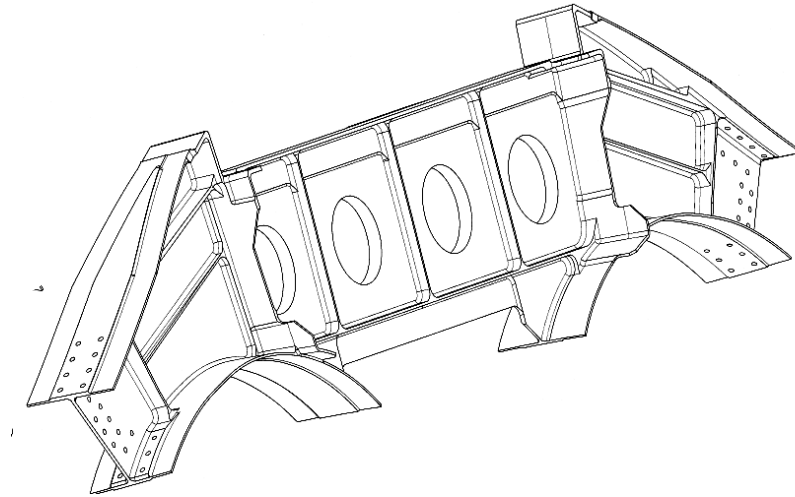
Типовая конструкция детали ”Траверса”
